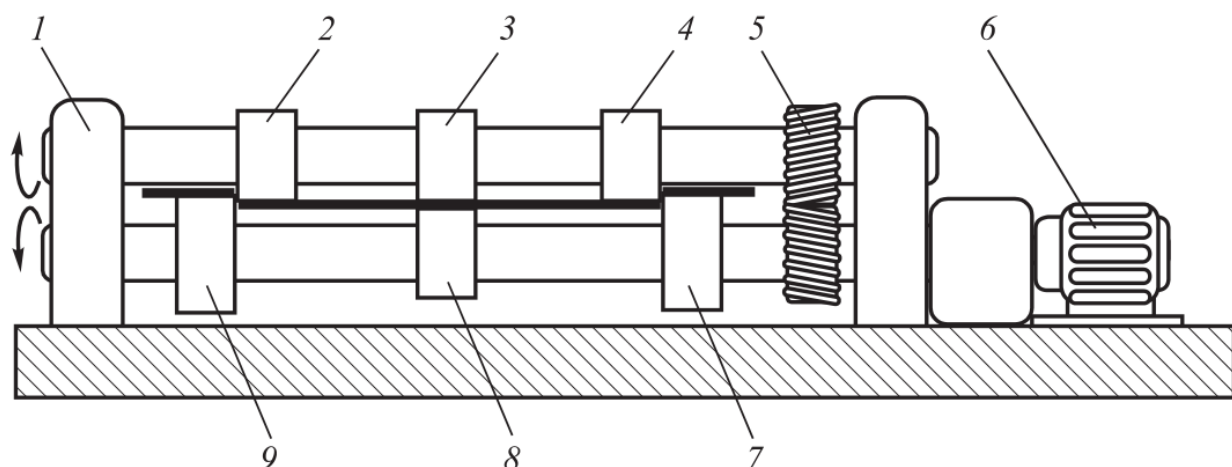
Схема дисковых ножниц для резки боковых кромок: 1 — станина; 2, 4, 7, 9 — режущие дисковые ножи; 3, 8 — опорные диски; 5 — шестерня; 6 — электропривод.
